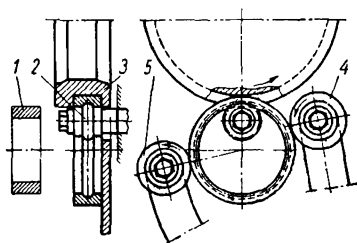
Схема открытого способа раскатки кольцевых заготовок: 1 — раскатываемая заготовка; 2 — центральный раскаточный валок; 3 — вращающийся нажимной валок; 4 — направляющий ролик; 5 — контрольный ролик
